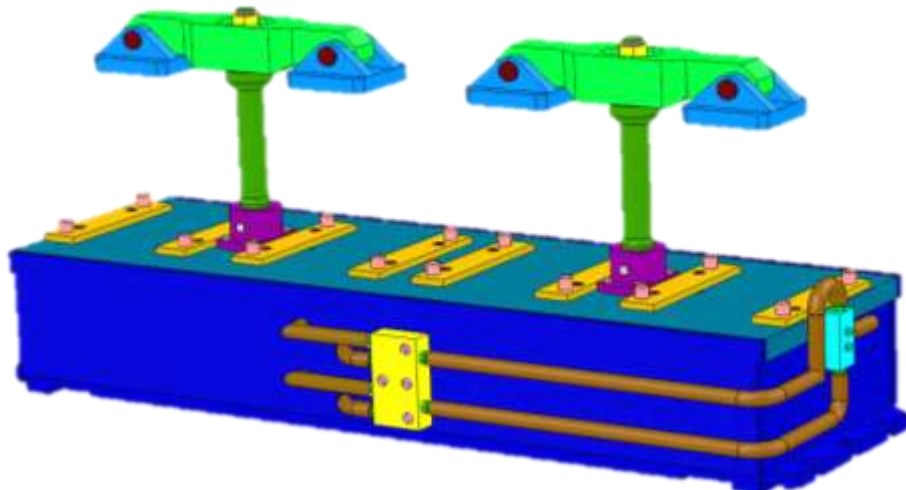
Пристосування для чистового фрезерування корпусів редукторів.
